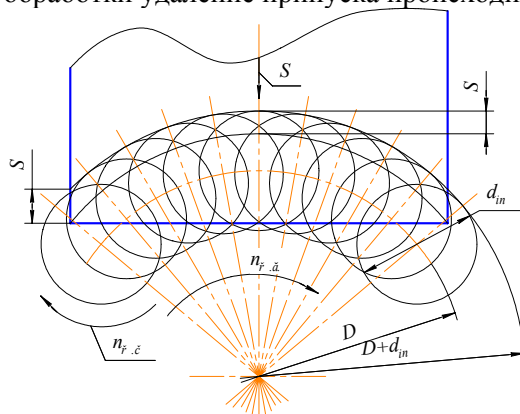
Схема удаления припуска с двумя главными вращательными движениями
